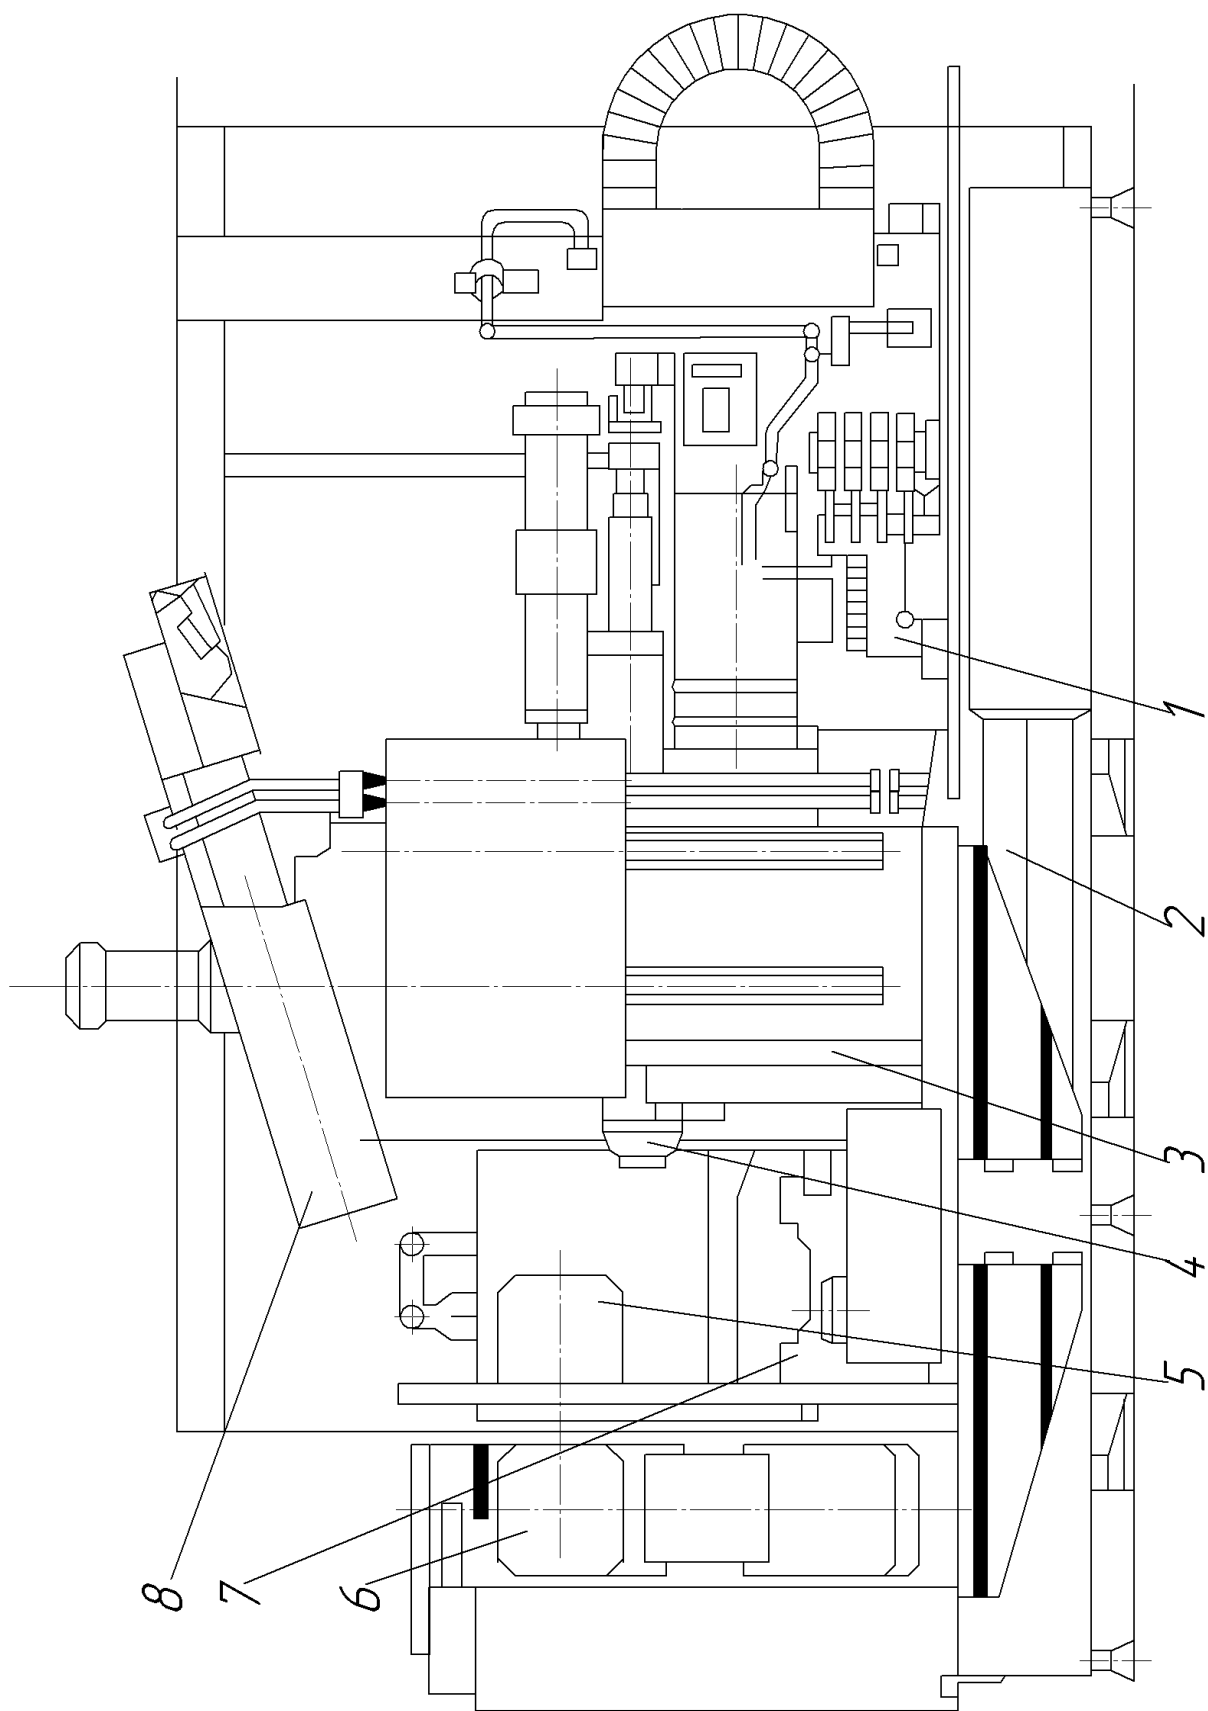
Загальний вид верстата моделі ІР320ПМФ4
